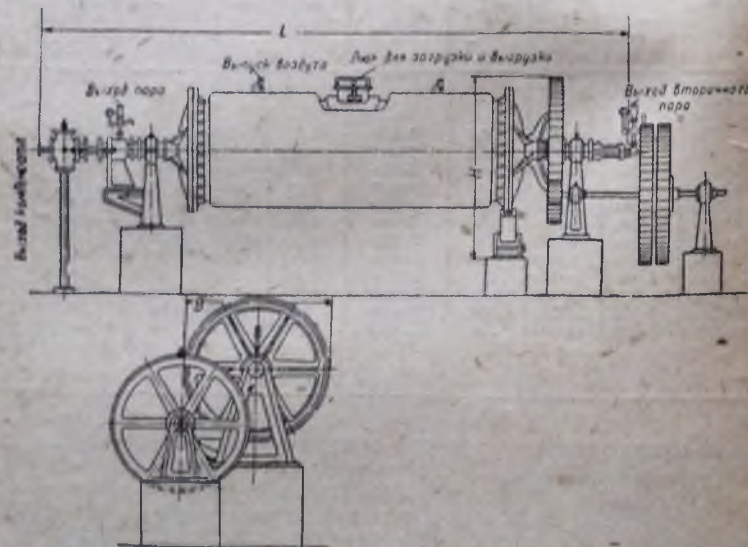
Гребковая вакуум-сушилка с вращающимся корпусом.
